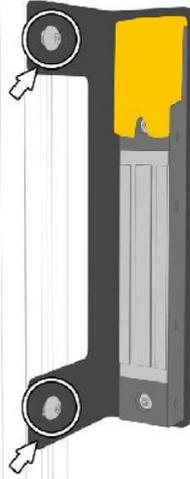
Montageplatte mit Prozesszuhaltung am Profil anbringen und und Schrauben M8 x 12 mm Torx festziehen.
